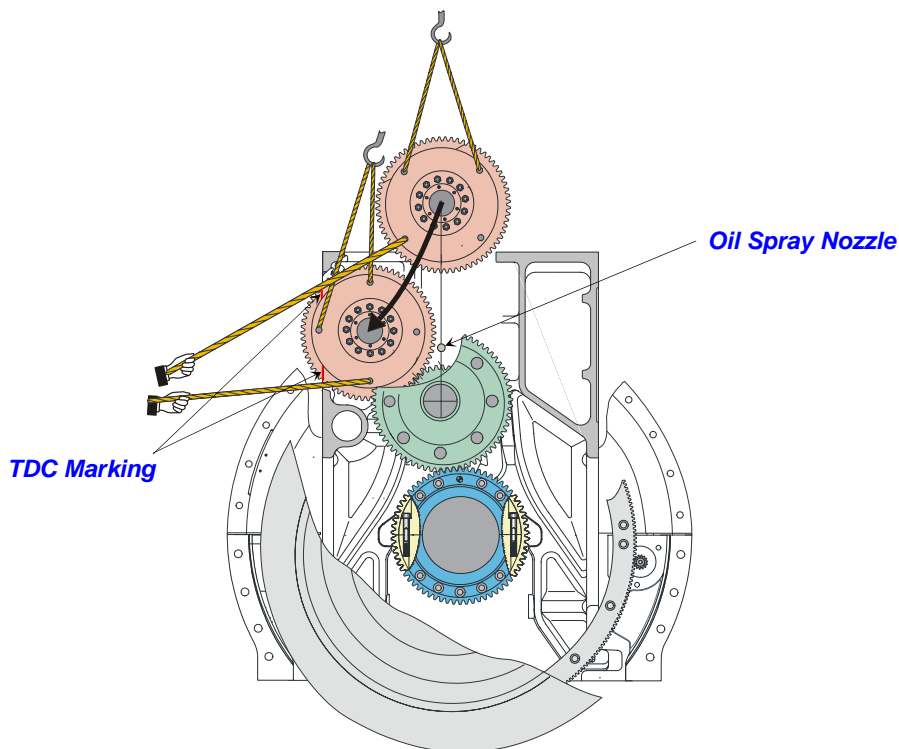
Mounting of the camshaft gear (캠 샤프트 기어의 조립)
